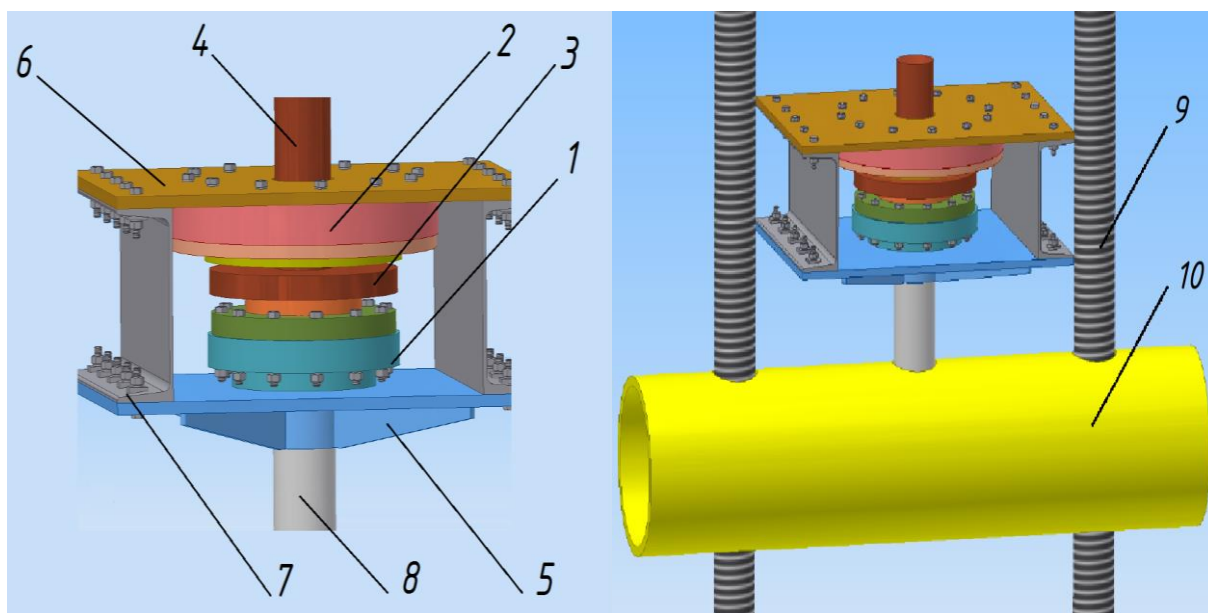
Конструкція ГМВМ: 1 – гідравлічний мембранний механізм; 2 – гідравлічний виконавчий механізм з отвором; 3 – фланець; 4 – шток зливку; 5 – нижня плита; 6 – плита верхня; 7 – швелер; 8 – шток барабана; 9 – гвинтова передача; 10 – барабан
